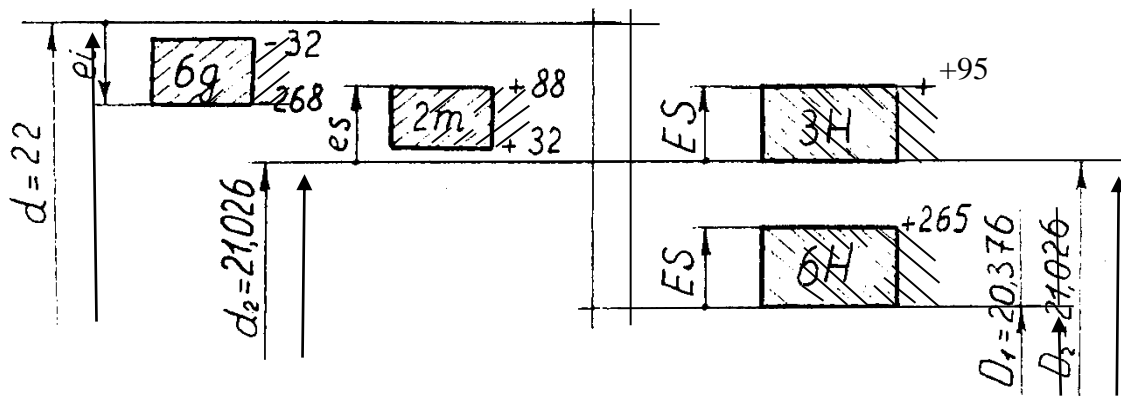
Схема расположения полей допусков метрической резьбы с переходной посадкой
